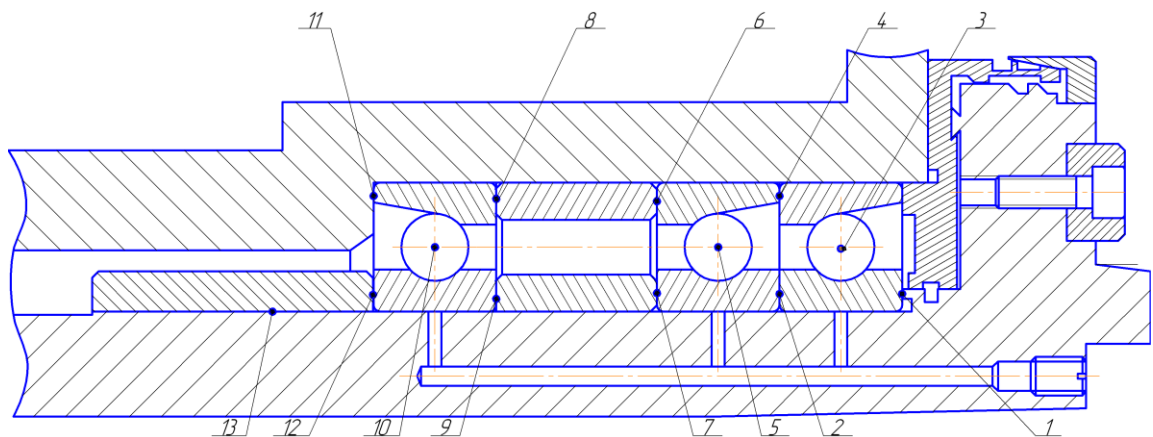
Конструктивна схема передньої опори шпиндельного вузла
